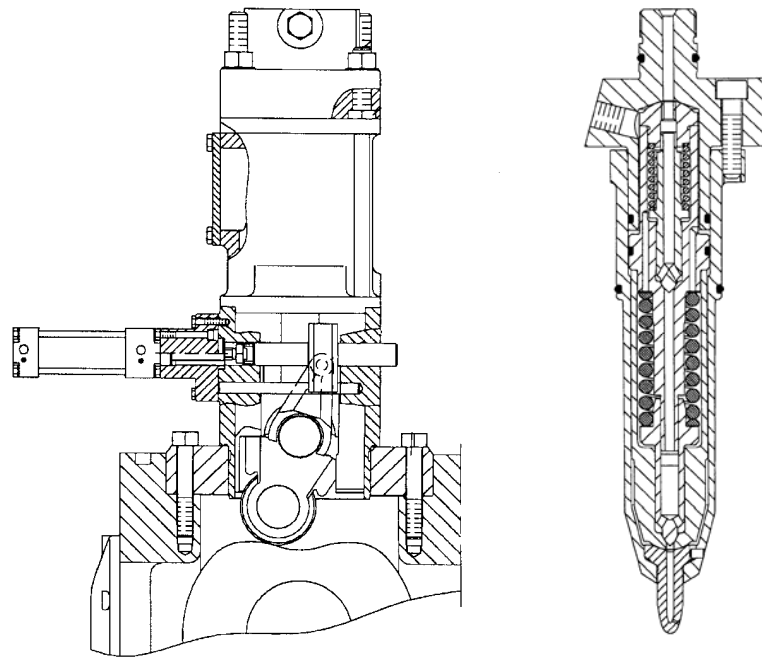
ПНВТ із механізмом реверса й форсунка [2].
